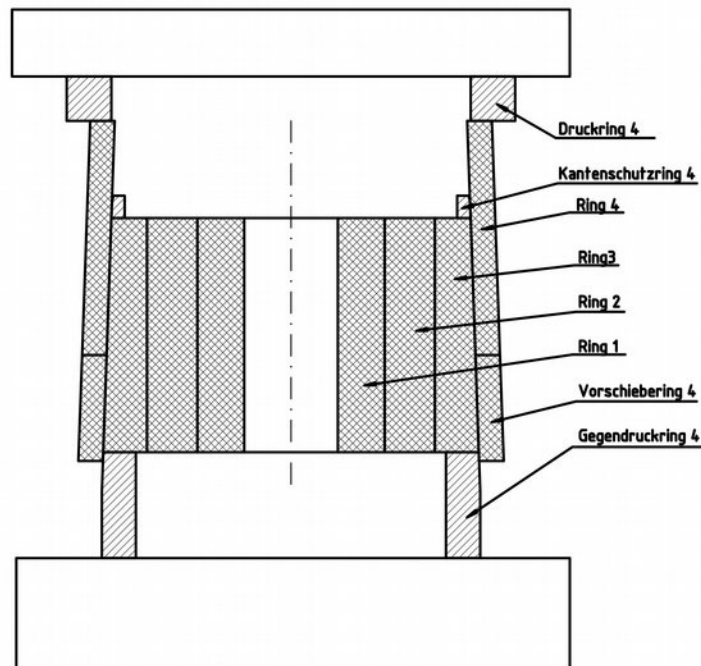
Hilfsformen für die Montage eines Multiring Schwungrads
